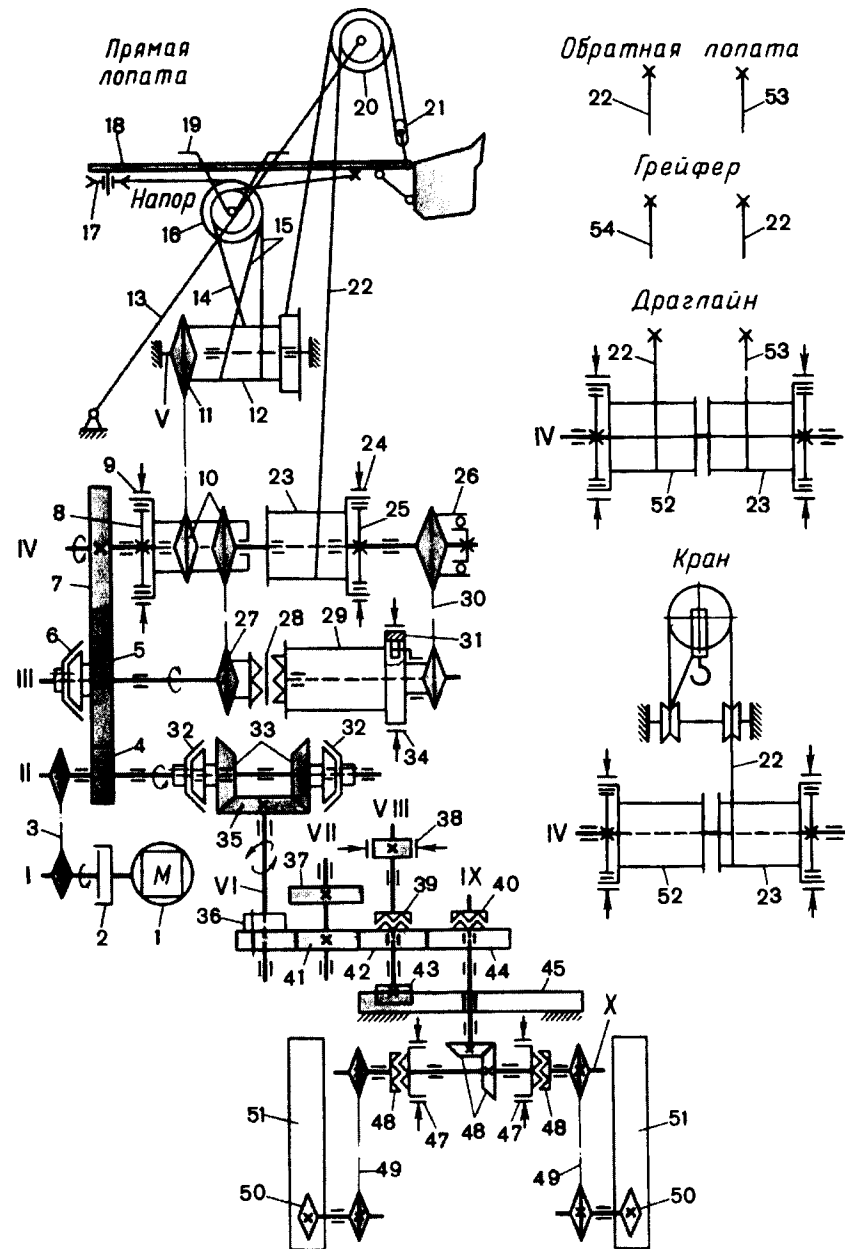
Типовая кинематическая схема одноковшового строительного экскаватора четвертой размерной группы с механическим приводом
